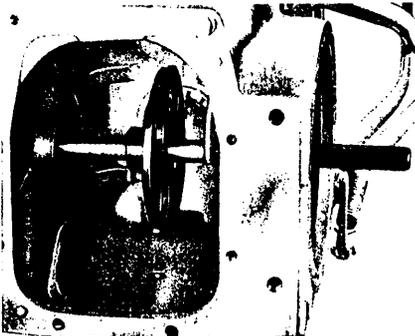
Vue arrière de l'outil A 137010 pour le réglage du couple conique.
